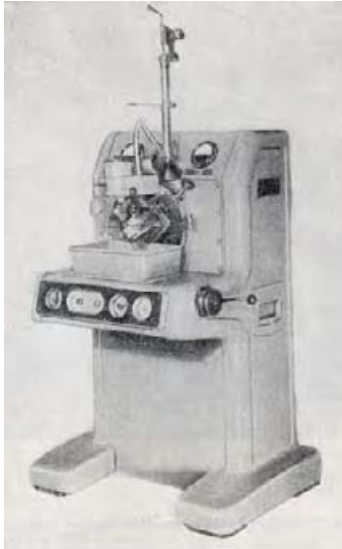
Сверление отверстий  $\varnothing 0,15$  мм в распылителях для насос-форсунок на быстроходном сверлильном станке с пневматическим приводом
